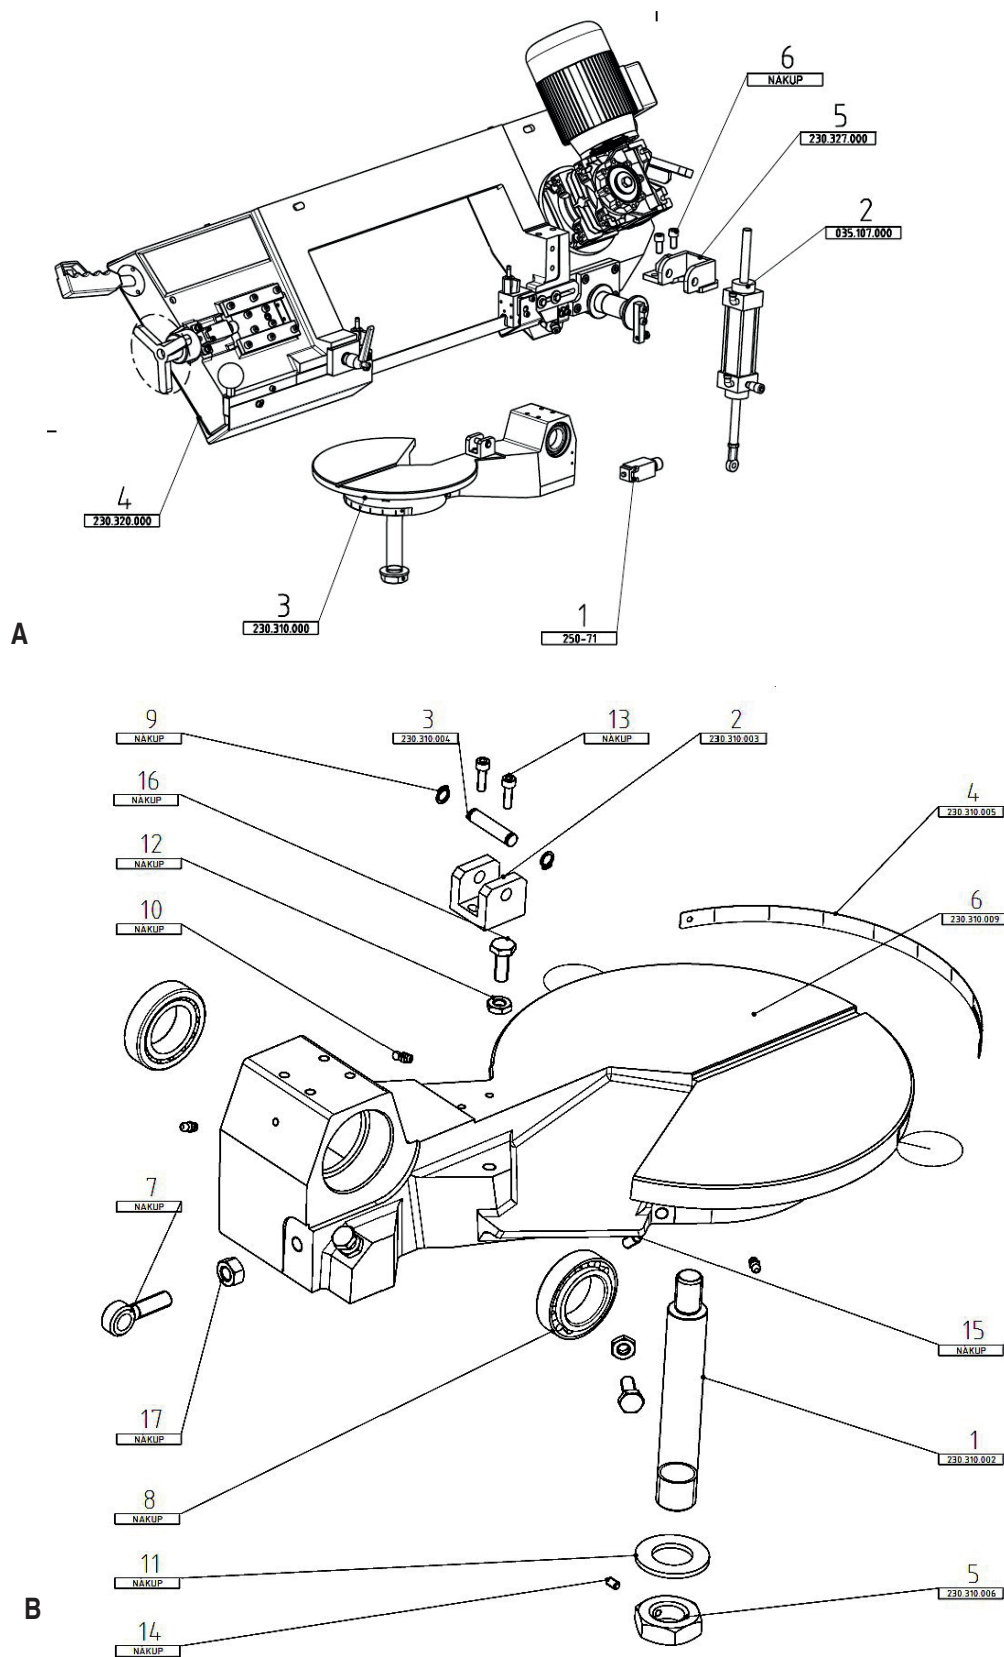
Dessin des pièces détachées 4 - A: Plan de travail avec bras de la scie - B: Plan de travail
